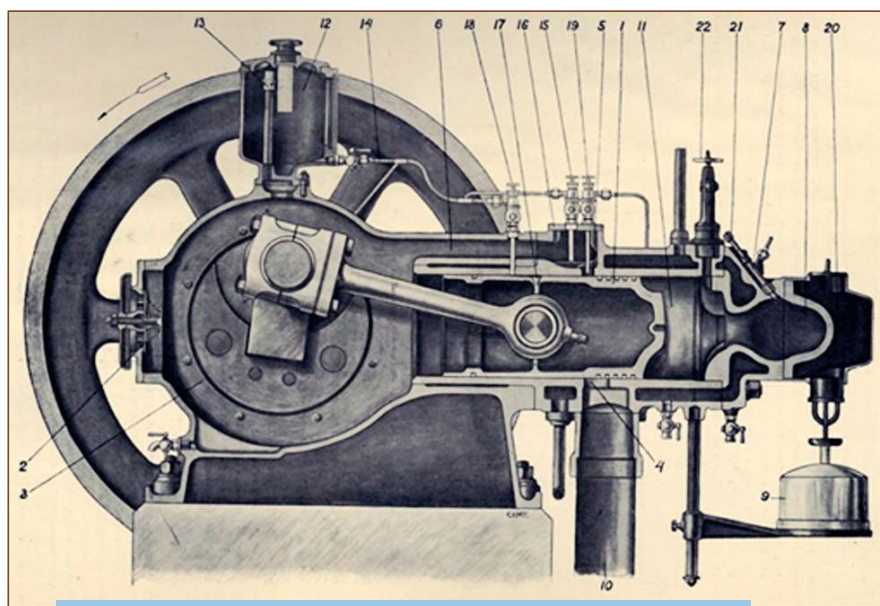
Продольный разрез нефтянки завода "Красный двигатель"
